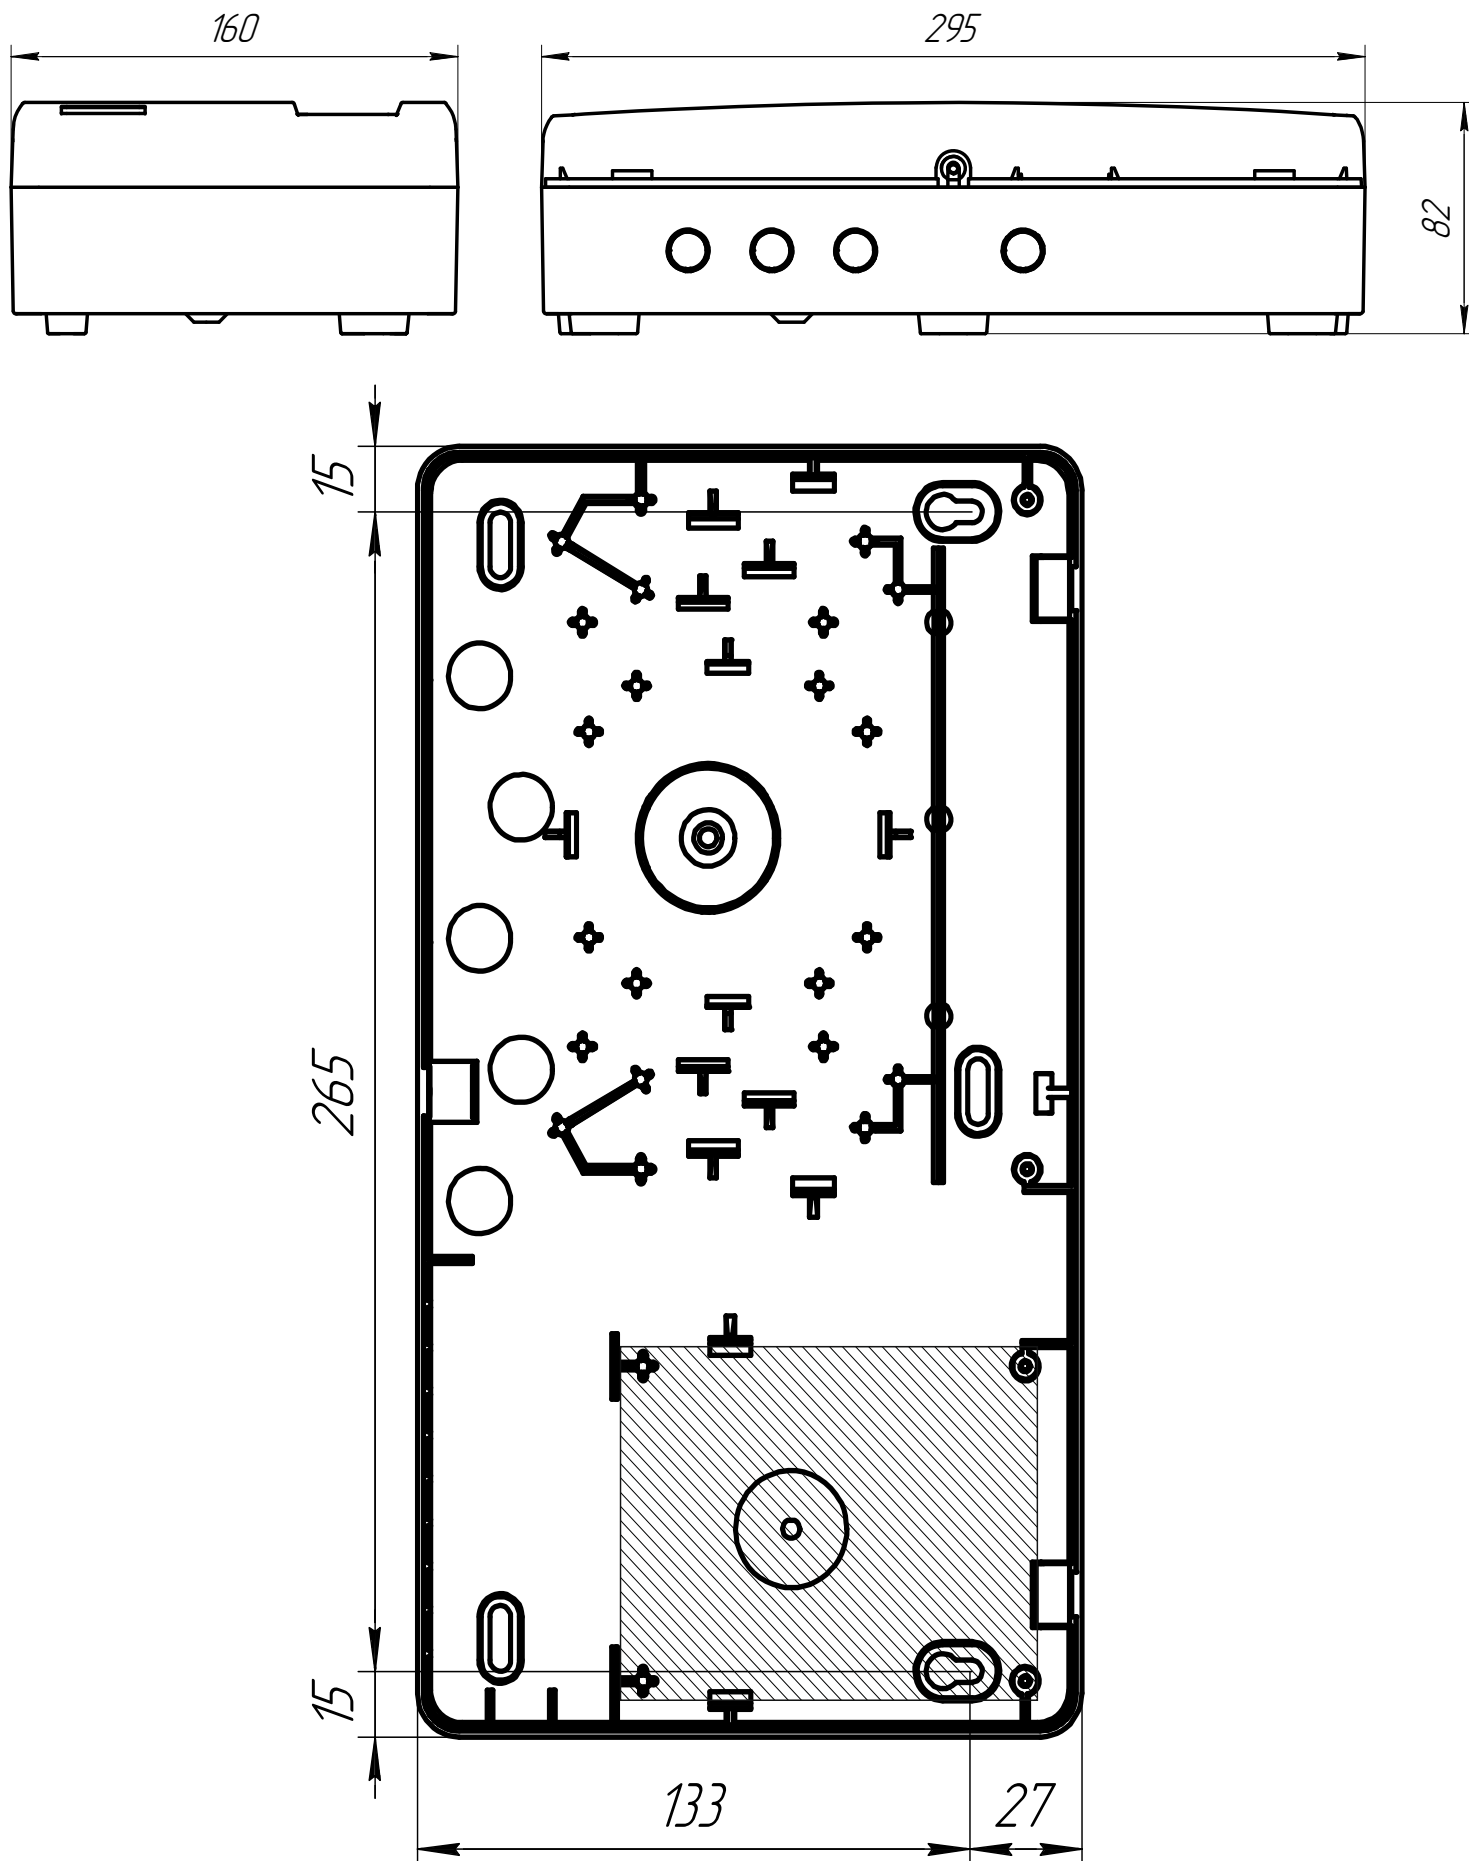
Корпус «Контакт» под АКБ 1,2 Ач
